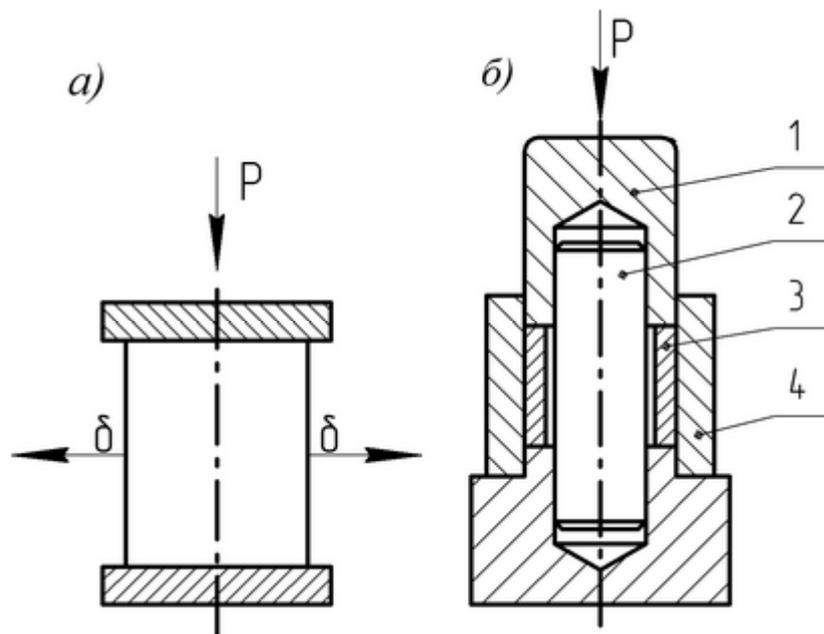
Осадка: а – схема обработки; б – приспособление для осадки втулок; 1 – пуансон; 2 и 4 – оправки; 3 – восстанавливаемая деталь
